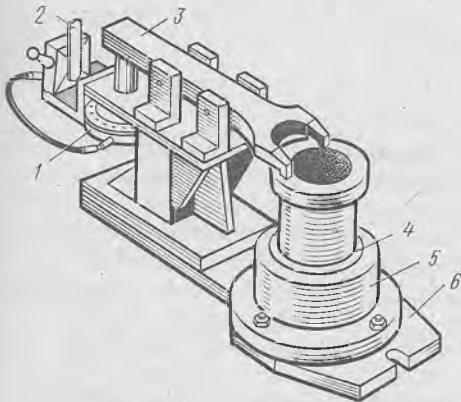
Приспособление для установки и крепления гильзы: 1 — пневматический привод; 2 — край управления; 3 — прижим; 4 — центрирующее кольцо; 5 — корпус; 6 — основание
